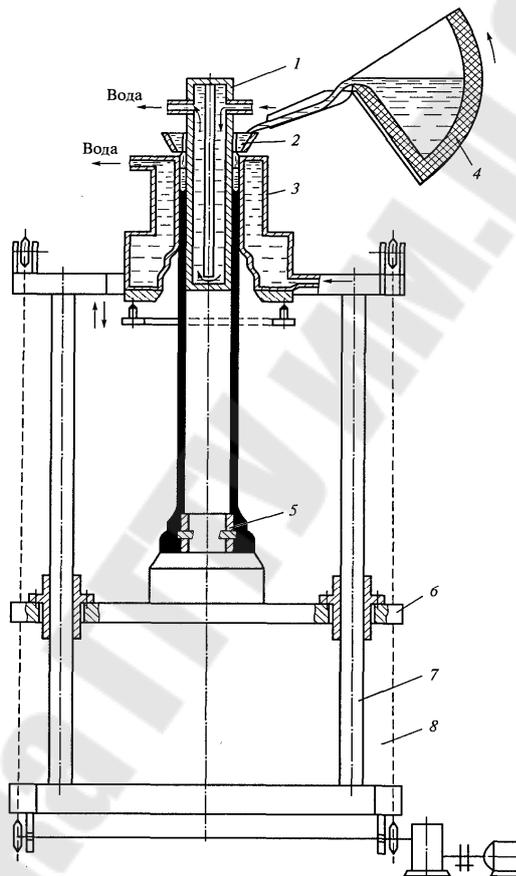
Установка полунепрерывного литья труб: 1- водоохлаждаемый стержень; 2- литниковая система; 3- кристаллизатор; 4- дозирующий ковш; 5- разборный стержень с кольцевым выступом; 6- стол; 7- колонны; 8- цепь привода стола
